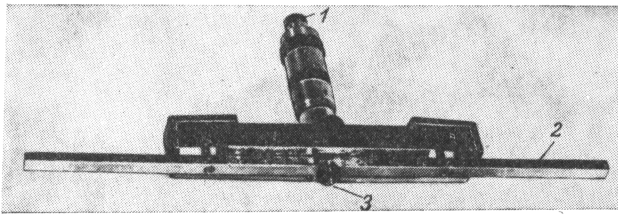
Приспособление для измерения стрелы прогиба ремня
